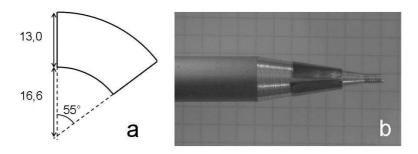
Dimensions de la feuille de cuivre (a), feuille enroulée autour du cône d'aluminium (b).
